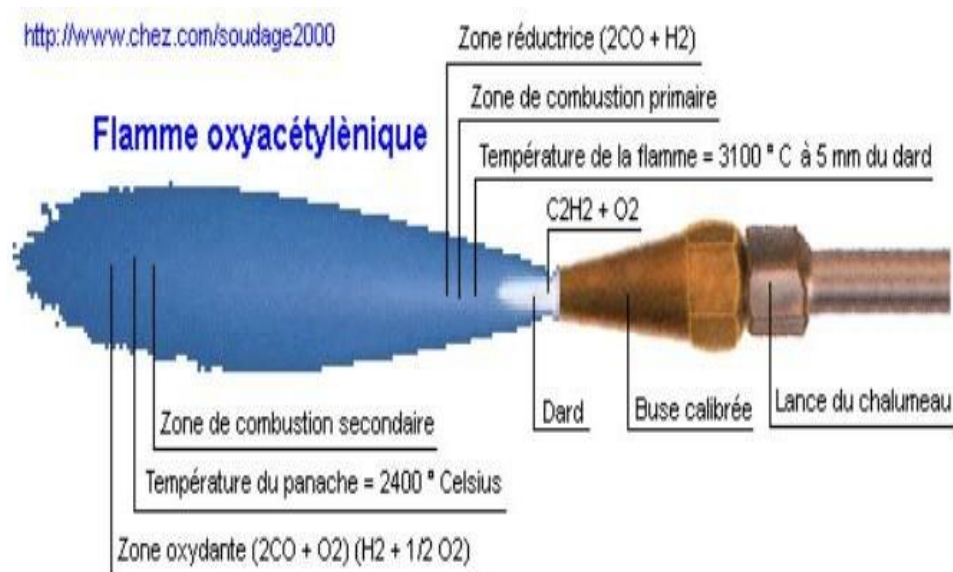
La flamme de soudage oxyacétylénique [6]
